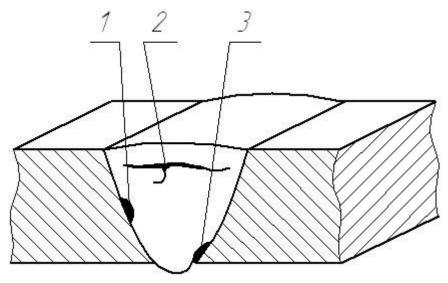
Виды горячих трещин при сварке
